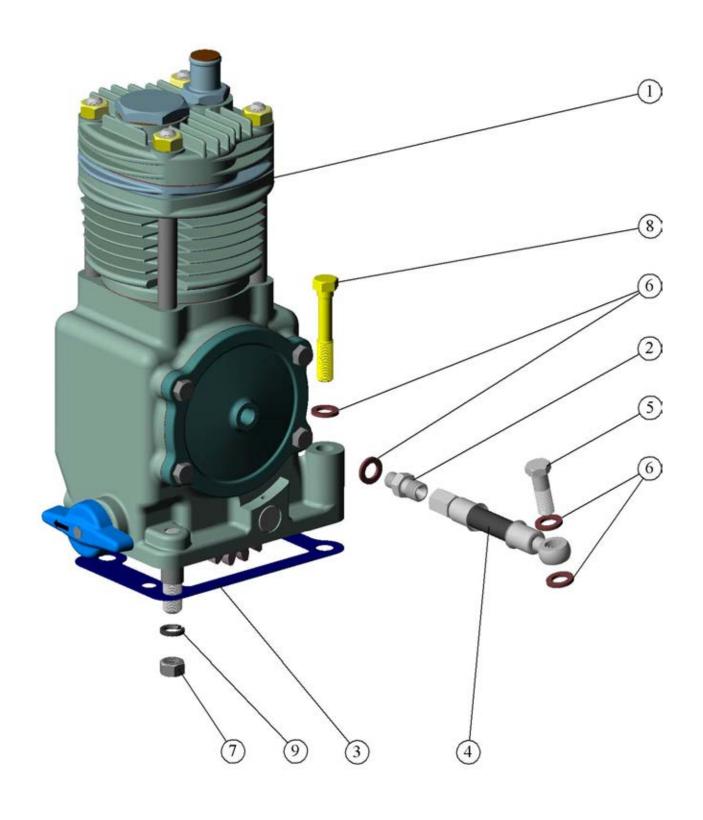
Установка пневмокомпрессора. Fig. 22 Pneumocompressor installation.
